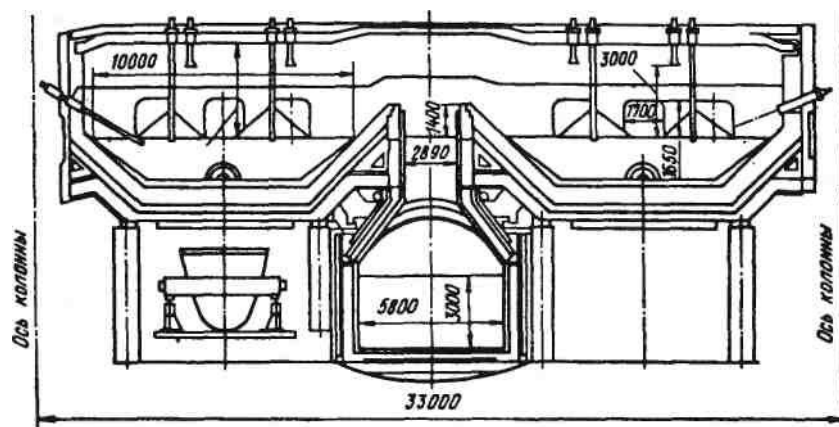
Одноканальный двухванный сталеплавильный агрегат Алчевского металлургического комбината (2*270 т)
